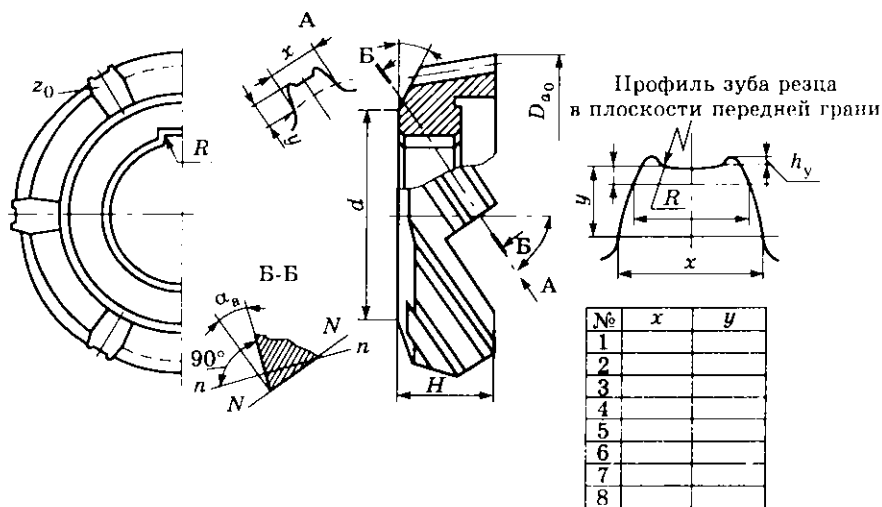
Конструктивные элементы обкаточного резца для обработки шлицевого вала
